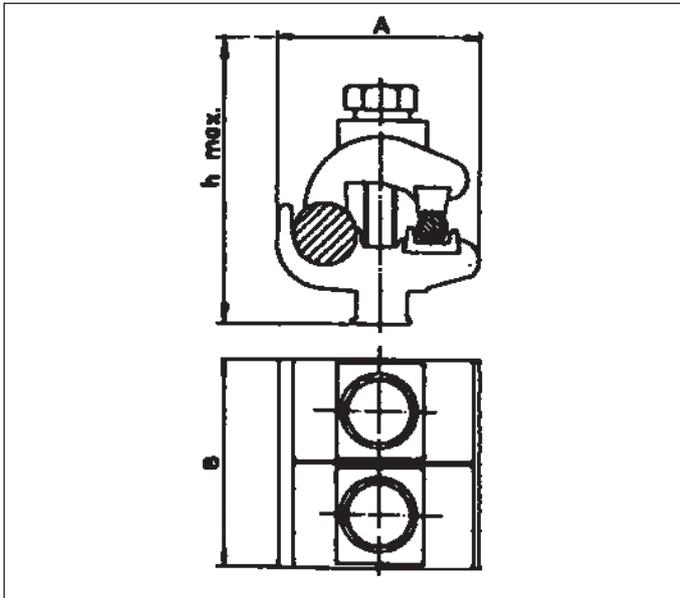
Конструкция переходного зажима: корпус из алюминиевого сплава и болты из защищенной стали, контактные поверхности из Al и Cu защищены эпоксидной краской.
